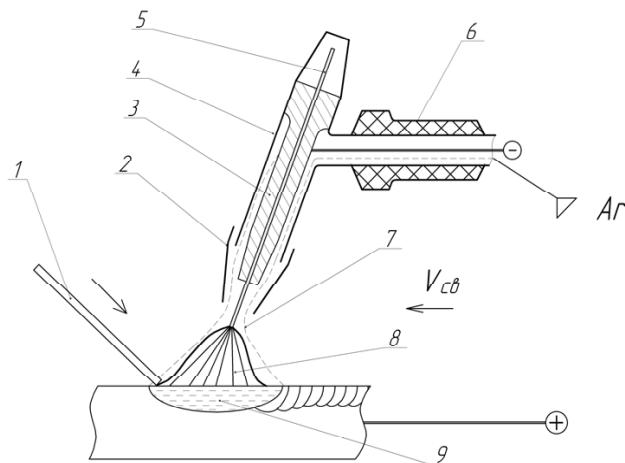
Схема аргонодуговой сварки неплавящимся электродом:
